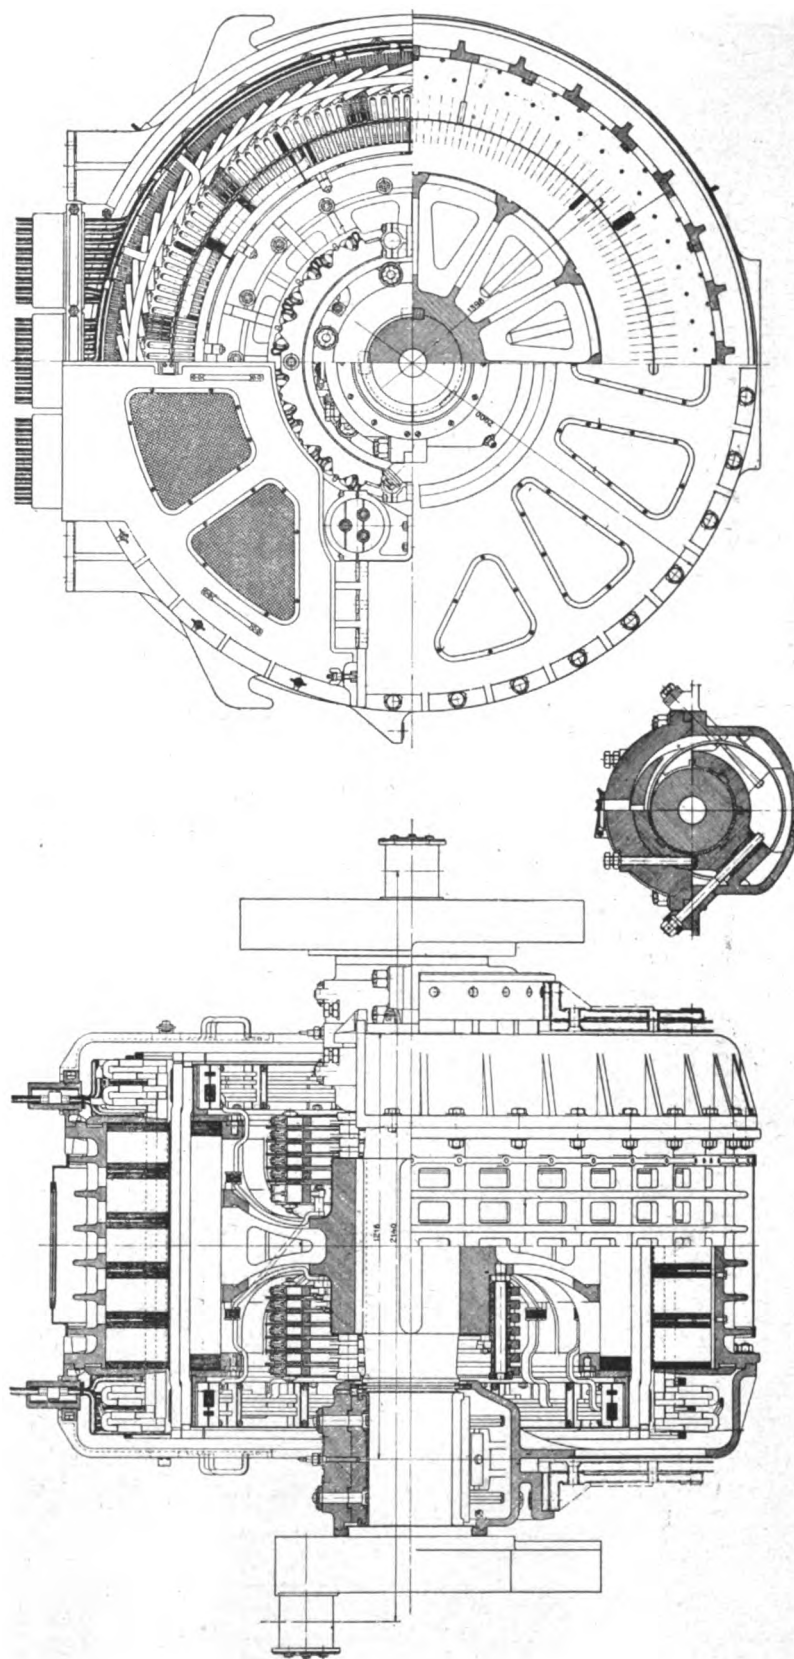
Insieme motore Loc. Gr. E. 432.
